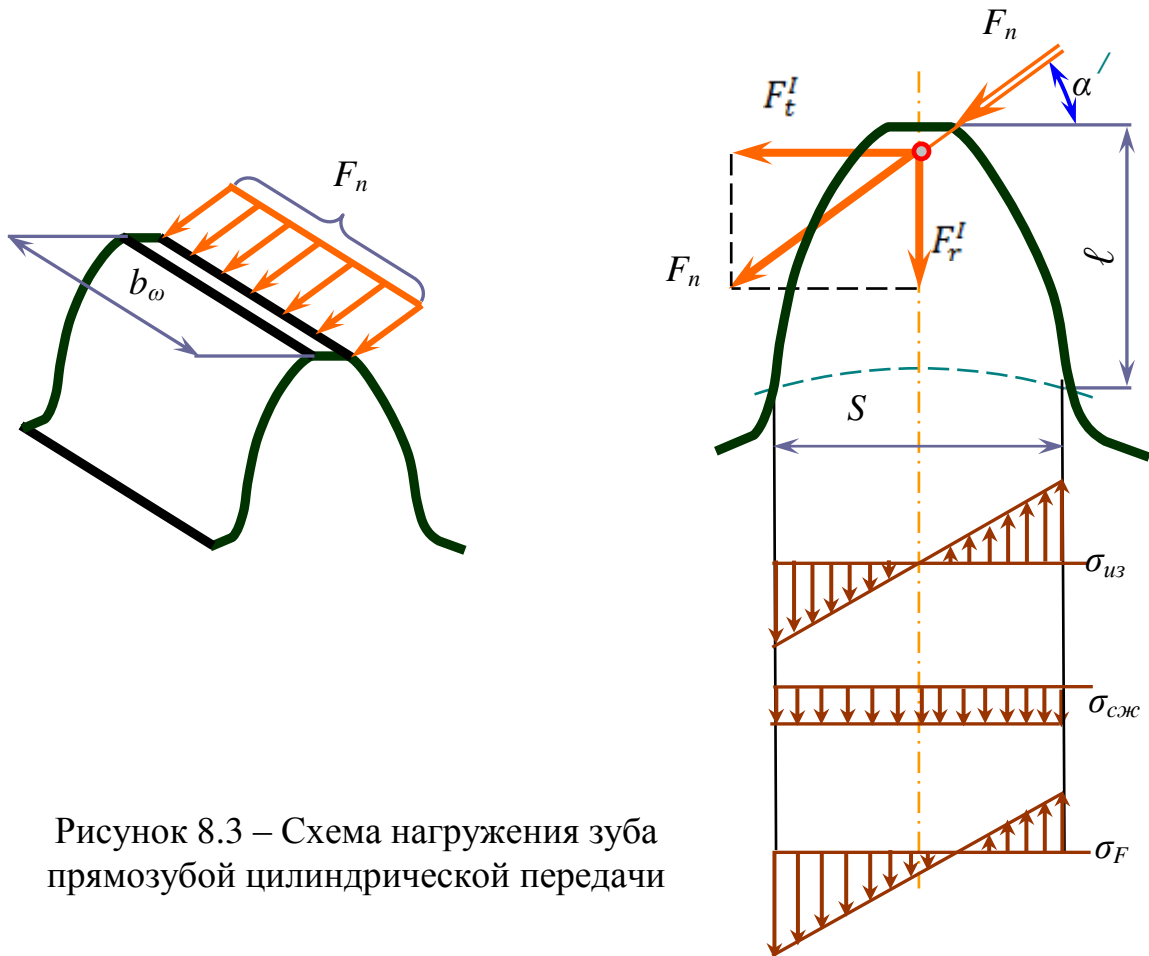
Схема нагружения зуба прямозубой цилиндрической передачи
